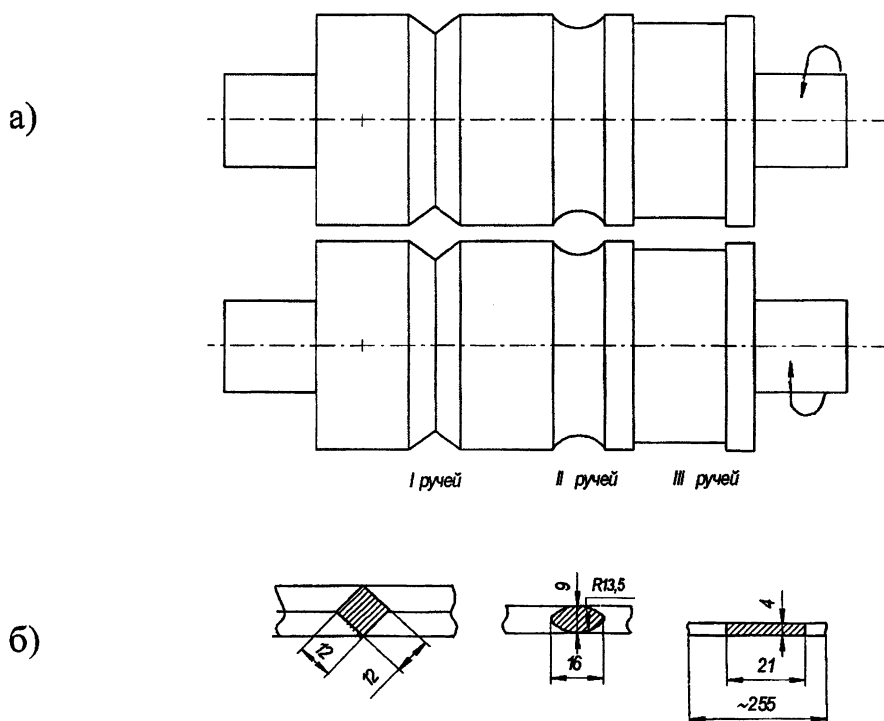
Схема прокатки — а) калибрующие валки; б) профили заготовки, получаемые в соответствующих ручьях валков
